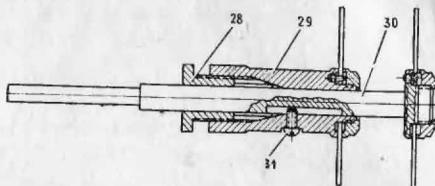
Оправка с двумя параллельными дисковыми пилами:
